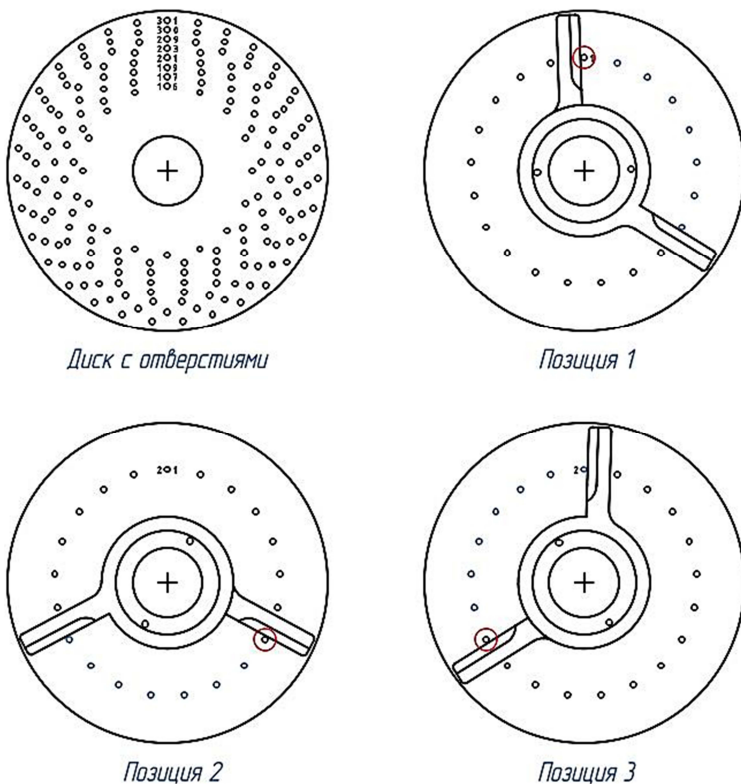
Пример работы УДГ и настройки делительного диска при делении заготовки на зубья
